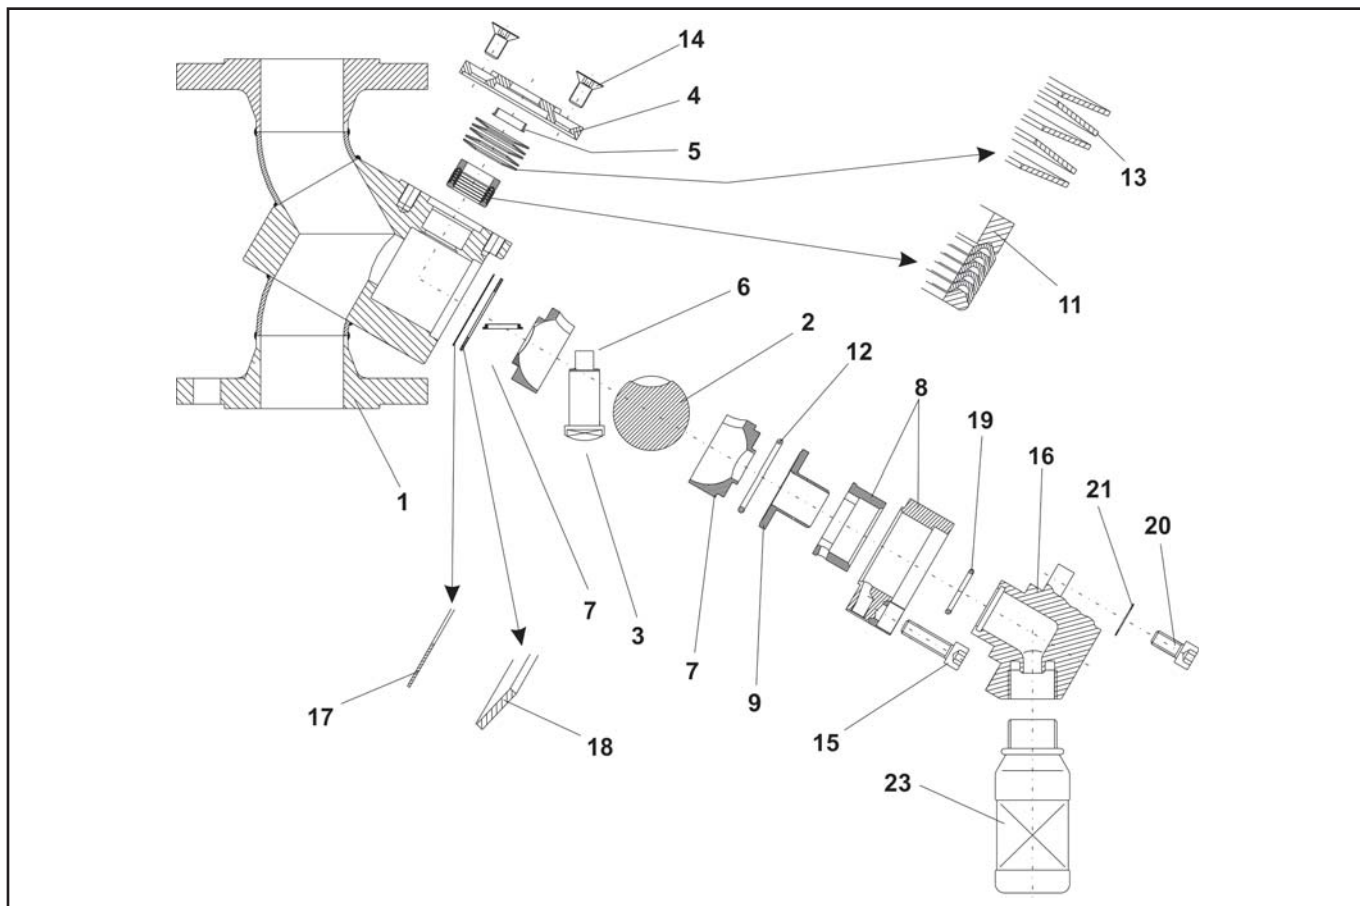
Сборочный чертёж пробоотборника BR 27g
